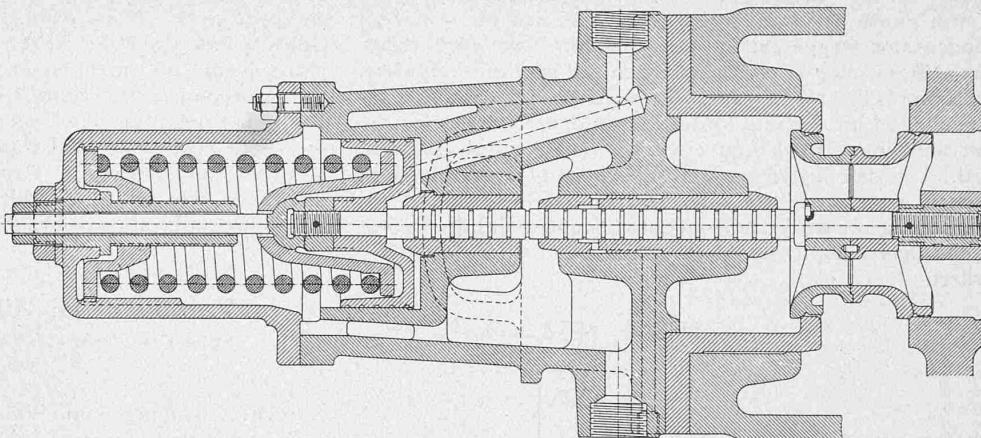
Doppelsitzventil einer Düsengruppe mit Druckölsteuerung der Tosi-Dampfturbine.
